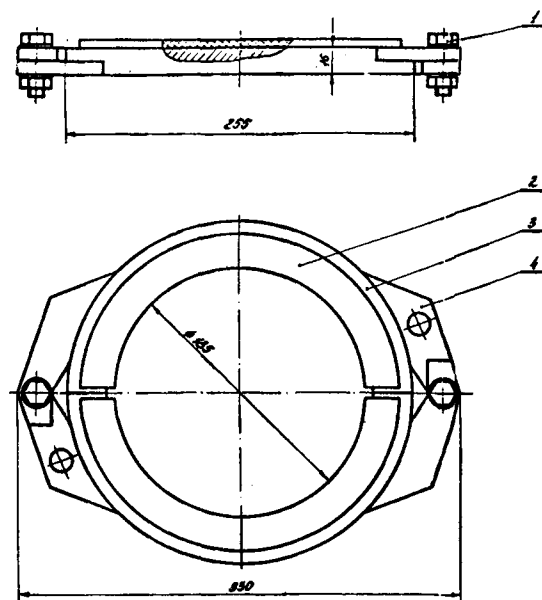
Приспособление для съема и установки омических делителей напряжения:
